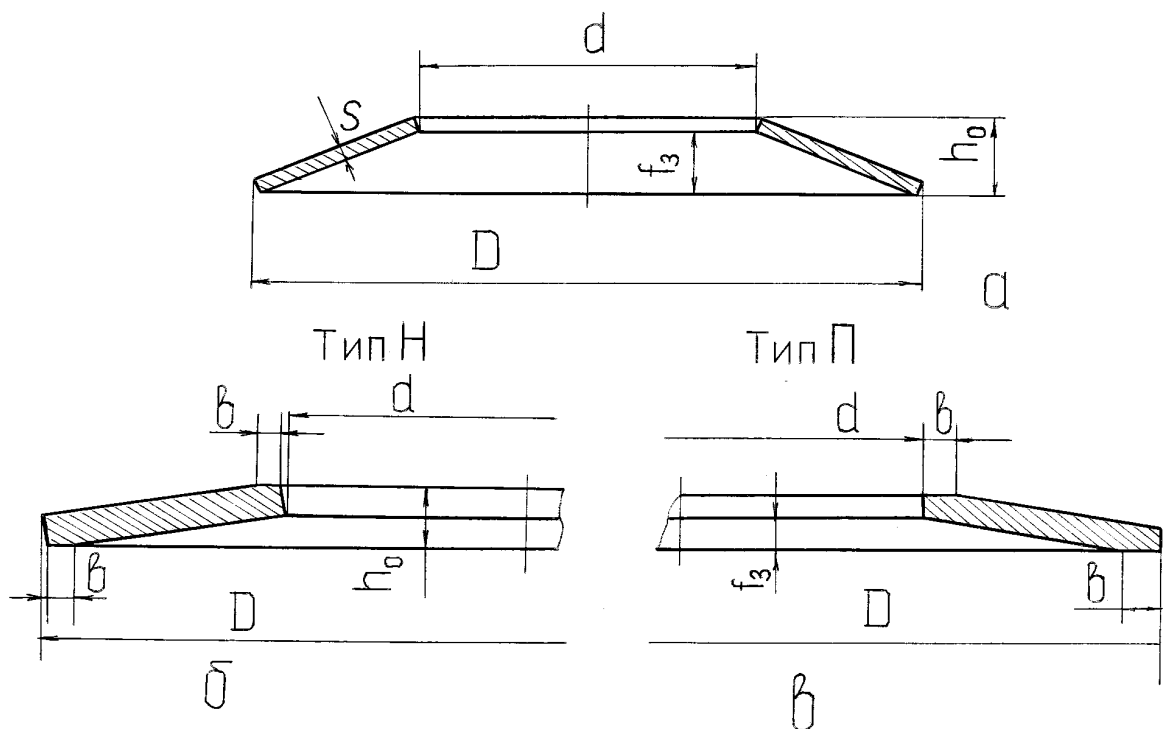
Розміри та ескізна коспоновка тарільчастих пружин: а, б – пружини нормальної точності, отримані штампуванням без механічної обробки поверхні обрізання, в – пружини підвищеної точності, отримані штампуванням з механічною обробкою поверхні обрізання
